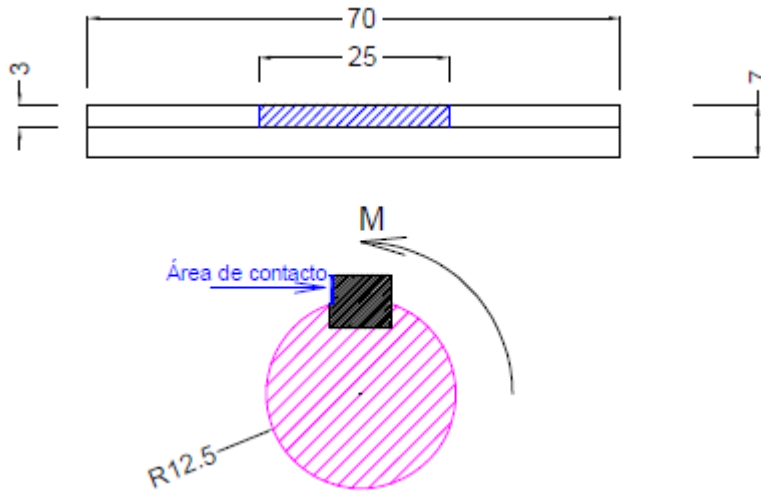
Aplastamiento. Eje de diámetro 25 mm.
